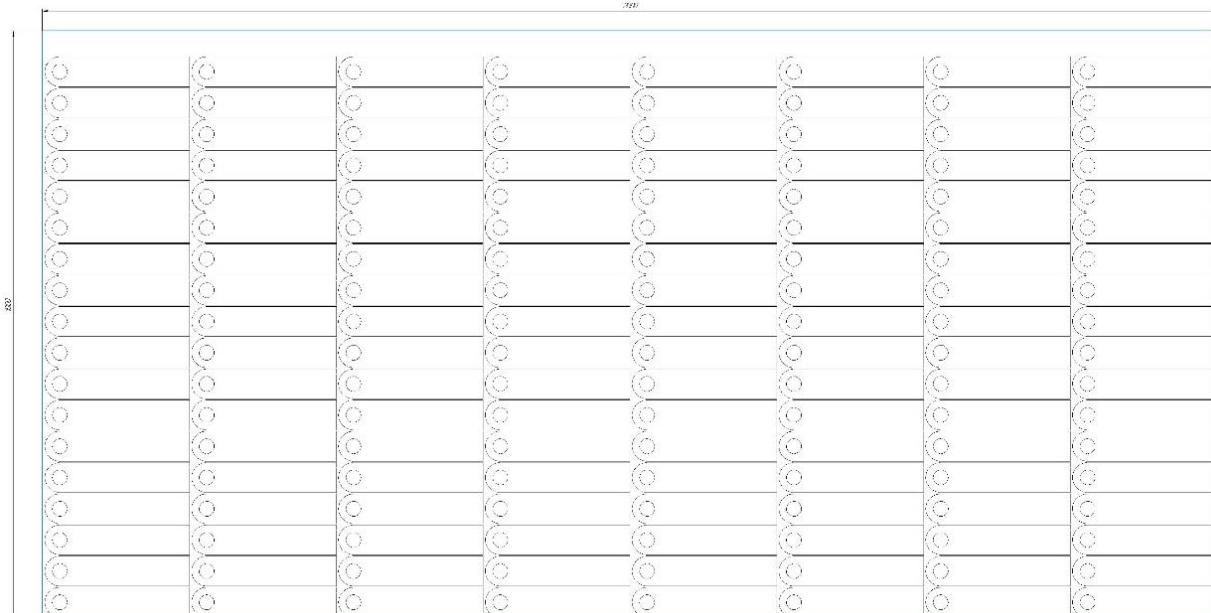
Кресленик заготовки деталі «Ніж Claas 998683 до кукурудзяної жатки»
